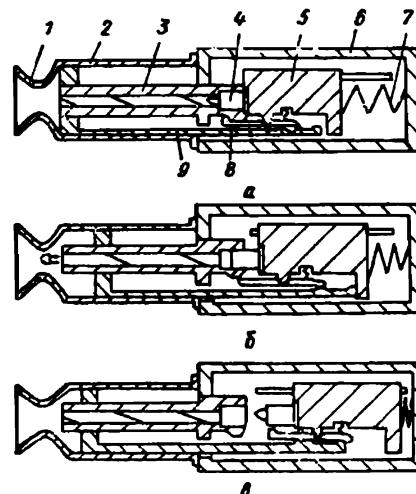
Схема автоматического оружия, работающего на принципе отвода части пороховых газов через дульное устройство:
